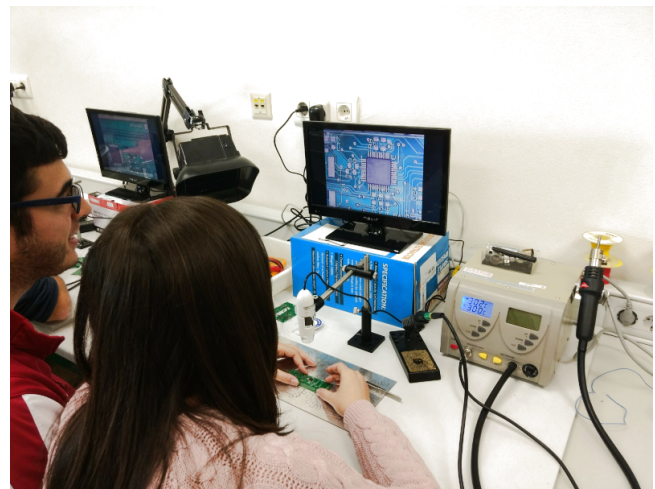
Uso de microscopio para realizar la soldadura SMD.
